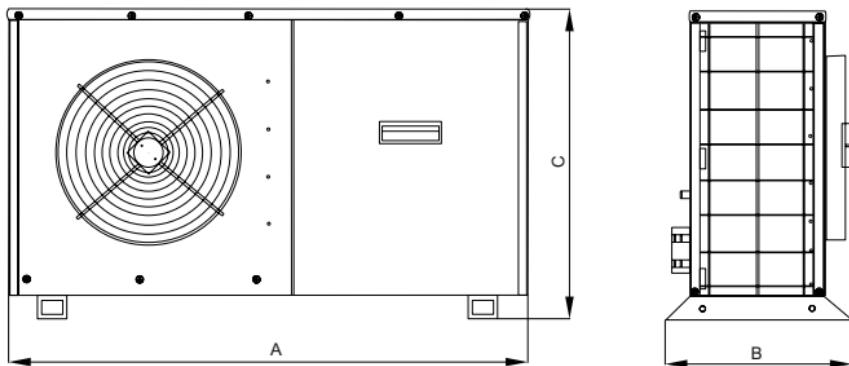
Габаритные размеры выносного конденсатора для типа AIR CAB /
